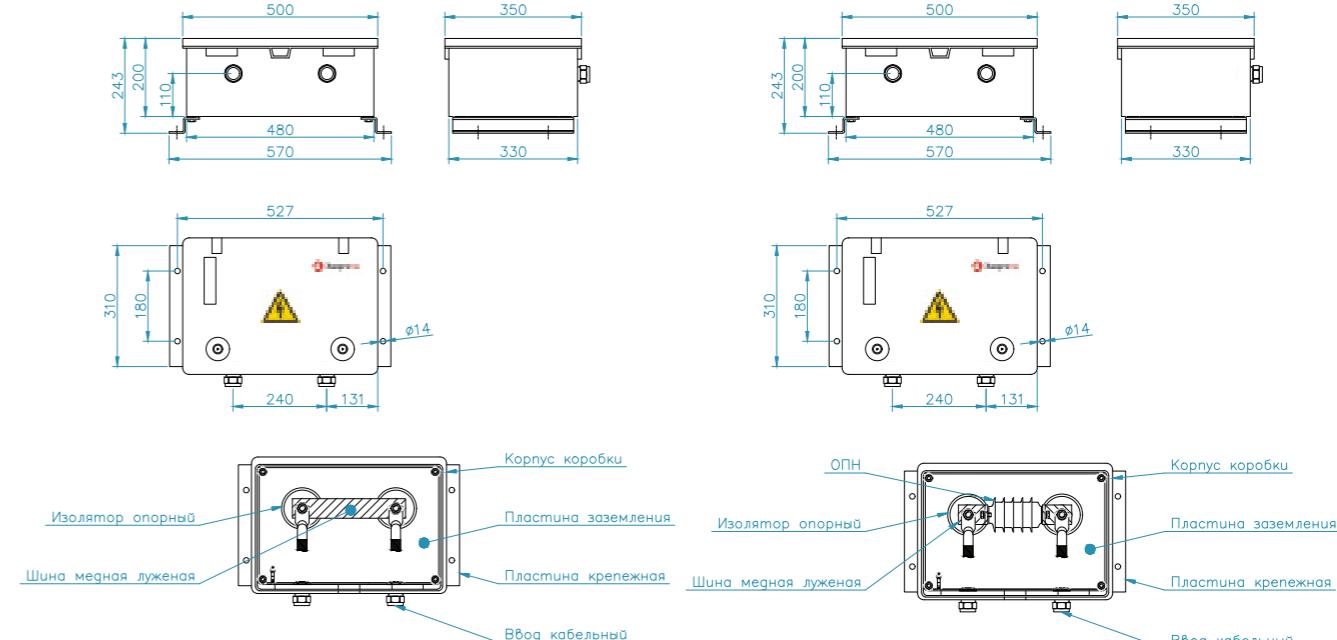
Чертеж коробки заземления ЭнергоТЭК КЗП-О
